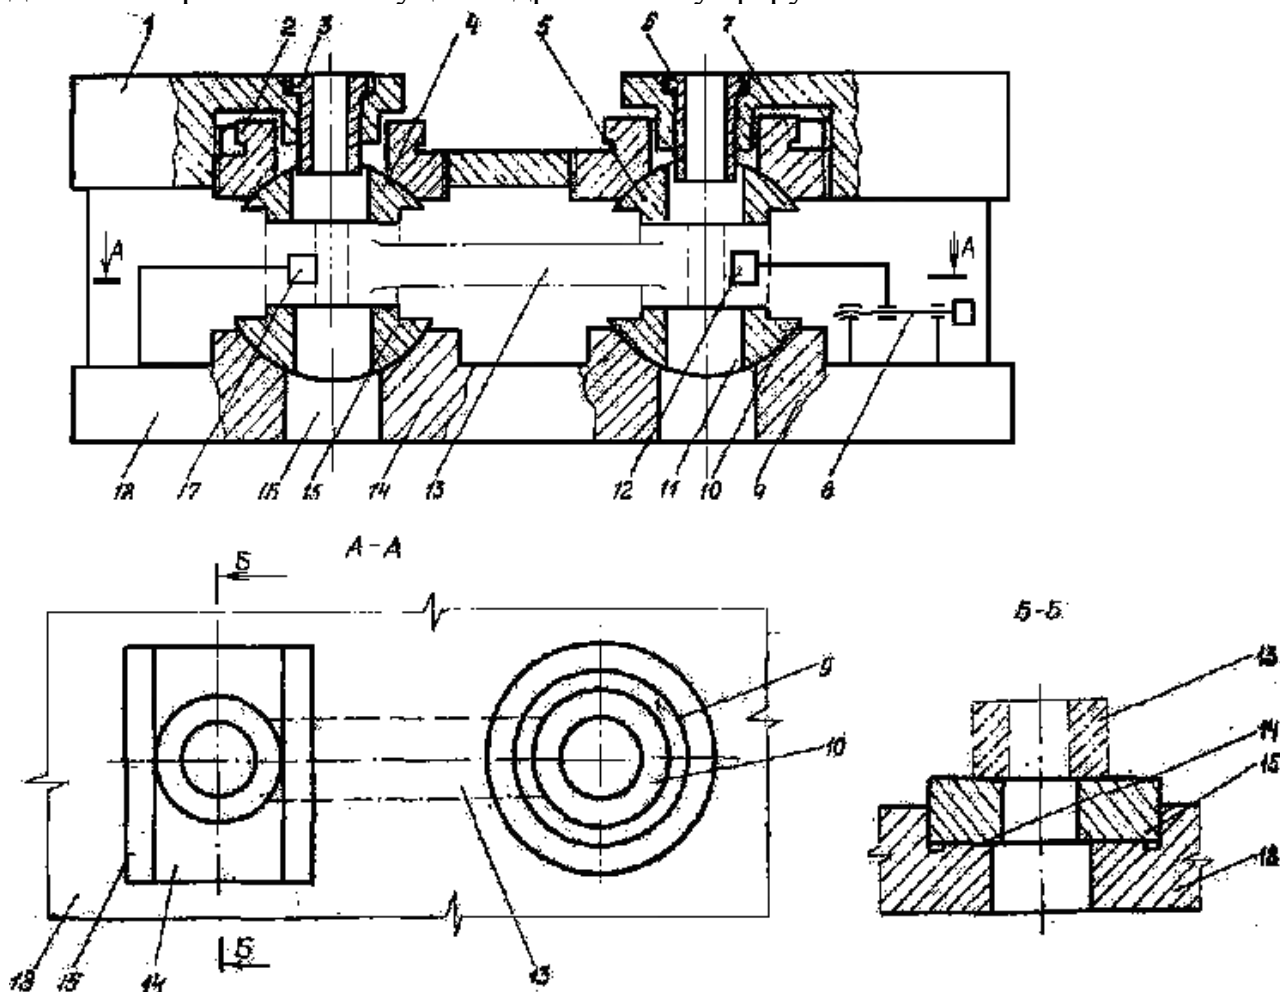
Кондуктор с самоустанавливающимися элементами
